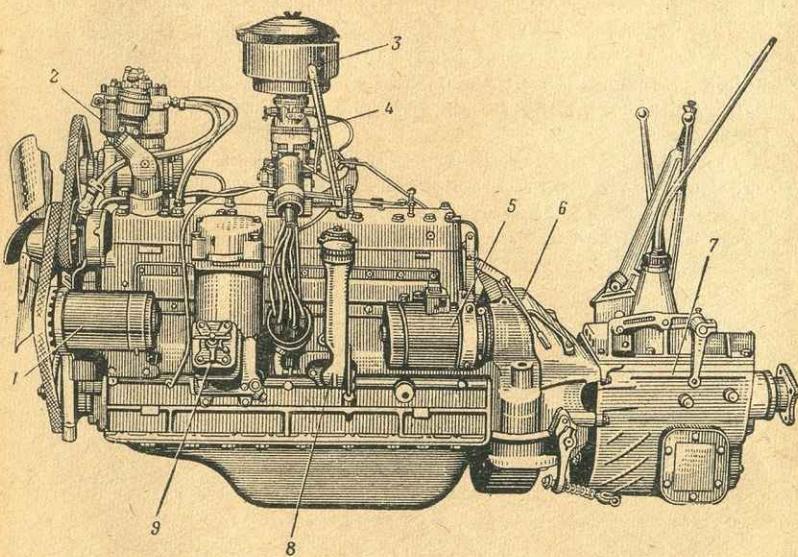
Двигатель со сцеплением и с коробкой передач (вид слева):
